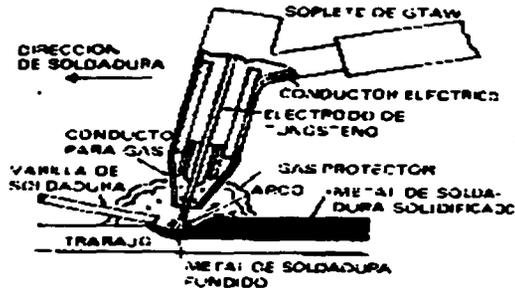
SOLDADURA CON GAS Y ARCO DE TUNGSTENO.
